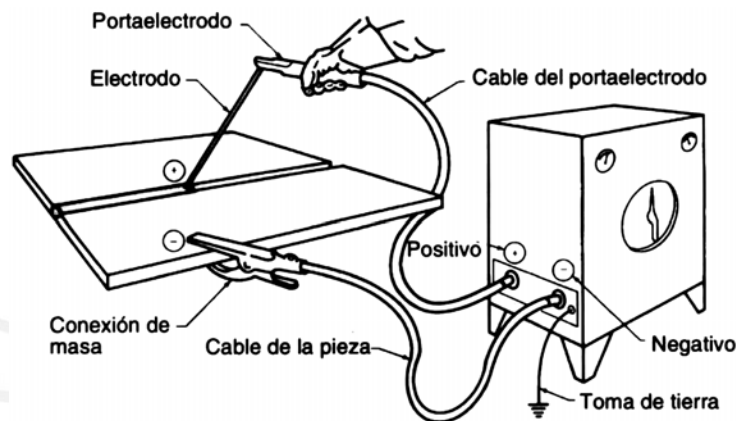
Proceso de soldadura SMAW [1]
